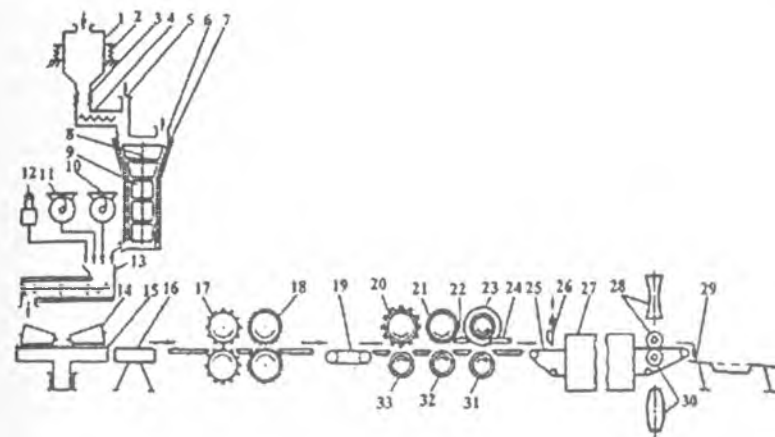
Участок приготовления корпусов конфет из грильяжной массы
